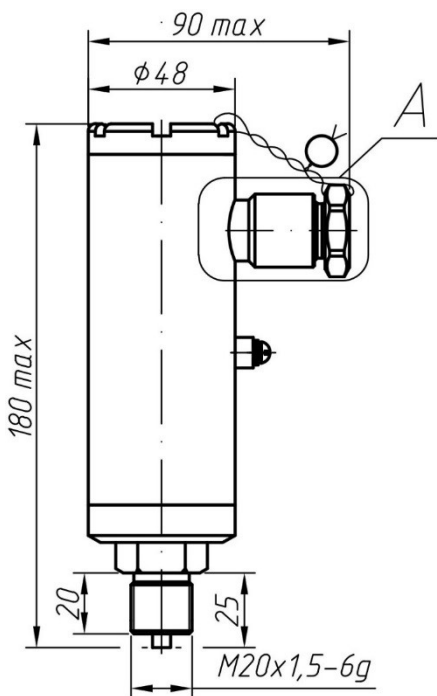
Габаритный чертеж датчиков-реле типа 1 по таблице 1
